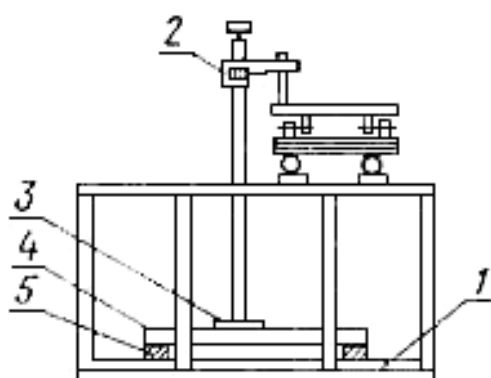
Приспособление для измерения высоты мягкого элемента:
